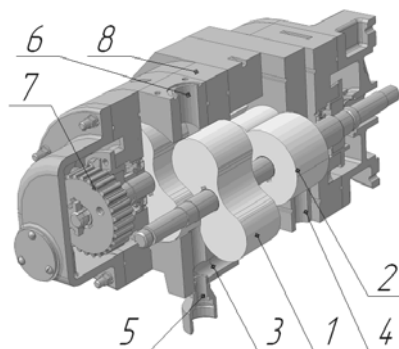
Экспериментальный агрегат на базе ступеней типа Рутс и КЗВН: 1– ротора типа Рутс; 2– кулачково-зубчатые ротора; 3– канал, соединяющий ступени; 4– выходное отверстие; 5 – патрубок для присоединения датчиков измерения давления и температуры между ступенями; 6– входное отверстие; 7 – синхронизирующие шестерни; 8 – межступенчатая перегородка
